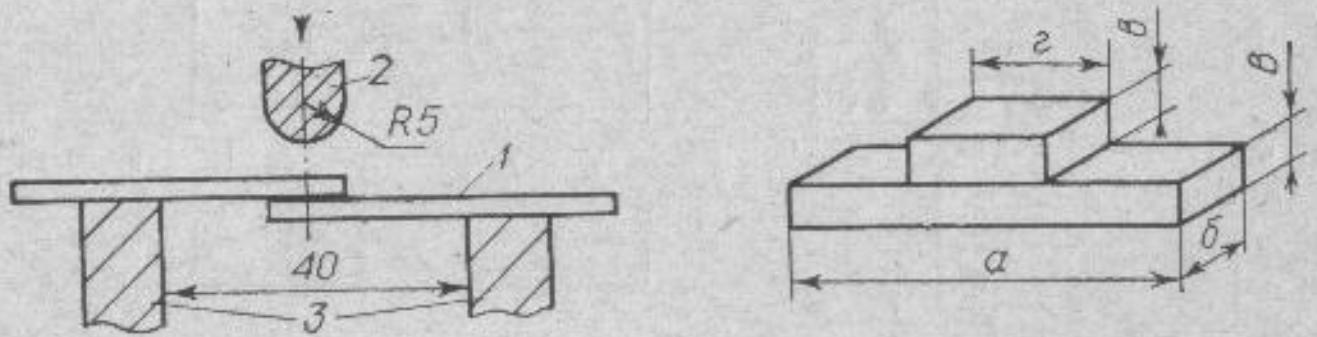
Схема испытаний kleевых соединений на неравномерный отрыв при изгибе:
